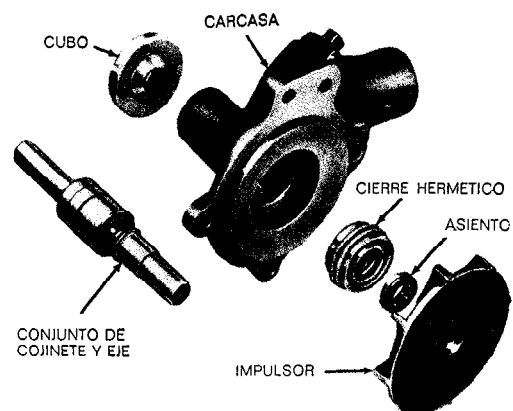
Despiece de una bomba de agua (Pontiac Motor Division of General Motors Corporation).
